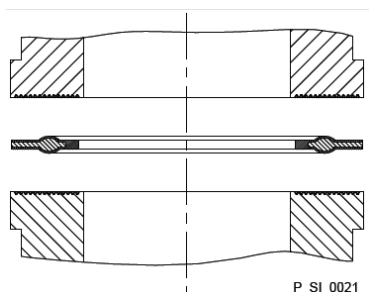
Литой композитный уплотнитель с ребристым вкладышем
